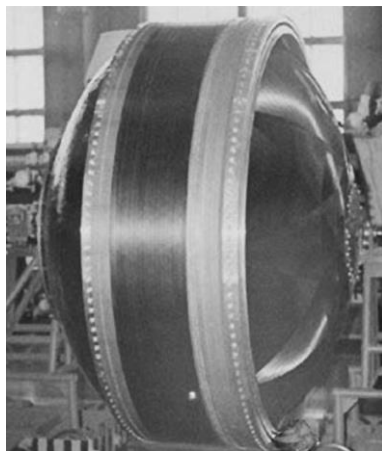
Корпус двигателя 3 ступени ракеты Р-39
